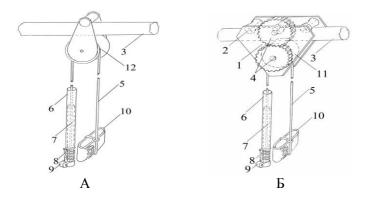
Тренажер № 3 (А – для обучения прыжку; Б – для совершенствования прыжка): 1 – корпус тренажера; 2 – опорный ролик; 3 – гимнастическая перекладина; 4 – шестерня; 5 – трос; 6 – часть шеста; 7 – направляющий вал; 8 – опорная пружина; 9 – датчик с возвратным механизмом; 10 – фиксирующий ремень; 11 – шкив; 12 – подвесной блок.
